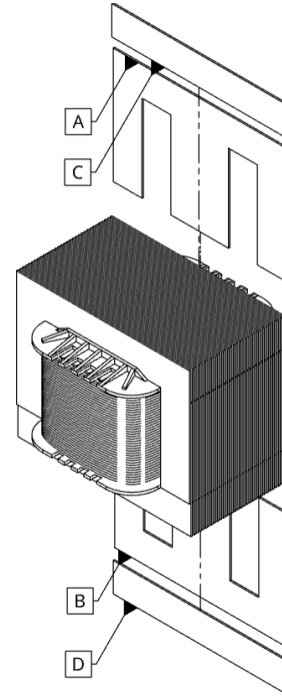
Plano de disposición de las laminas en el núcleo primero se alterna entre el paso A y B sucesivamente hasta que se tenga apretado el carrete y posterior se alterna entre el paso C y D.
